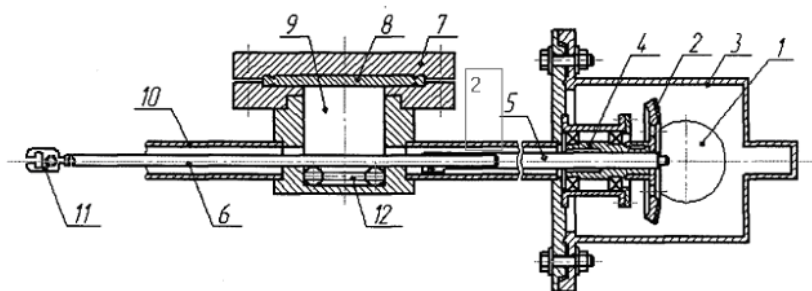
Шлюзовая камера: 1 — фланец для крепления высоковакуумного ввода вращения; 2 — коническая передача; 3 — корпус камеры системы передачи движения; 4 — гайка; 5 — ходовой винт; 6 - шток; 7 — фланец; 8 — медная прокладка; 9 — камера загрузки исследуемого образца с держателем; 10 — канал шлюзовой камеры для переноса образца в аналитическую камеру; 11 — оправка шлюзовой камеры для переноса образца; 12 — каретка
